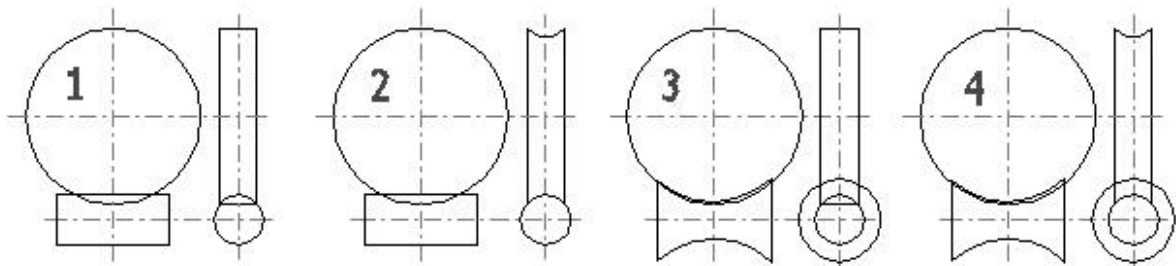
Tipos construtivos do conjunto sem-fim (MITCALC)
